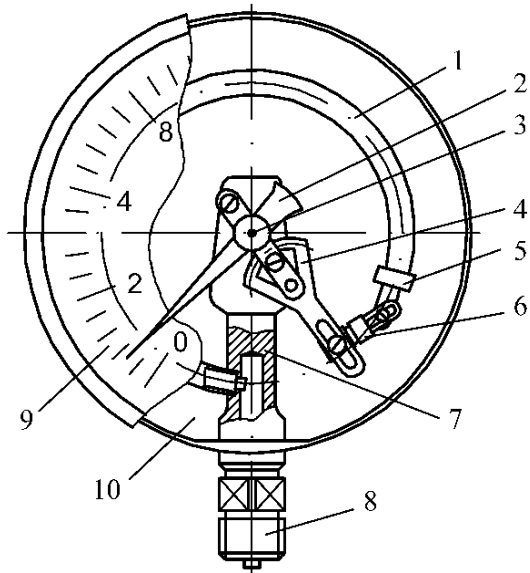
Деформаційний манометр з одновитковою трубчатою пружиною
